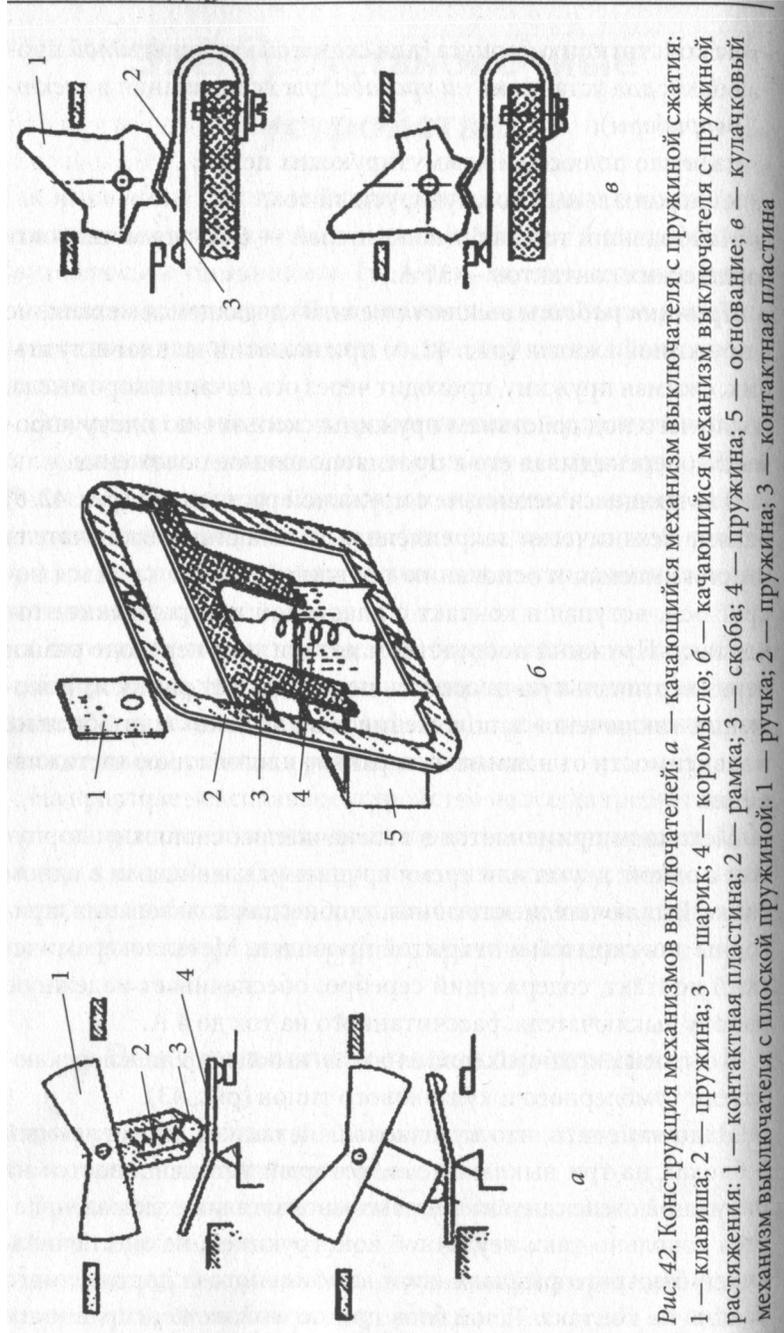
Конструкция механизмов выключателей: *а* — качающийся механизм выключателя с пружиной сжатия; 1 — клавиша; 2 — пружина; 3 — шарик; 4 — коромысло; 5 — шарик; *б* — качающийся механизм выключателя с пружиной растяжения; 1 — контактная пластина; 2 — рамка; 3 — скоба; 4 — пружина; 5 — основание; 6 — кулачковый механизм выключателя с плоской пружиной; 1 — ручка; 2 — пружина; 3 — контактная пластина
